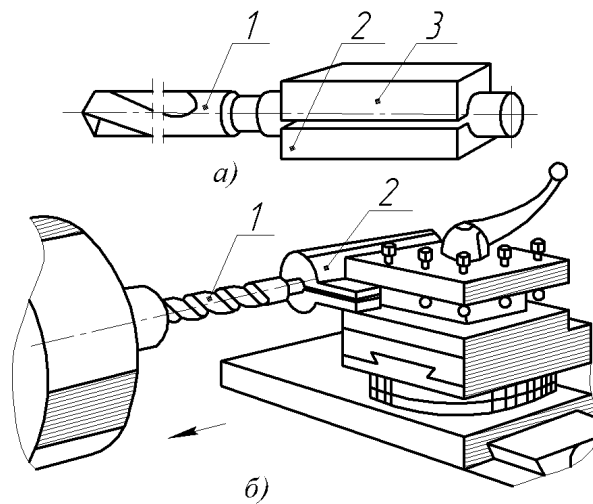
Свердління на токарному верстаті із закріпленням свердла в різцетримачі:
